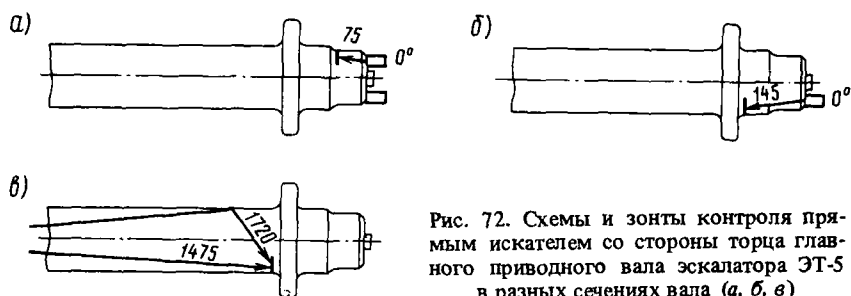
Схемы и зоны контроля прямым искателем со стороны торца главного приводного вала эскалатора ЭТ-5 в разных сечениях вала (а, б, в)
